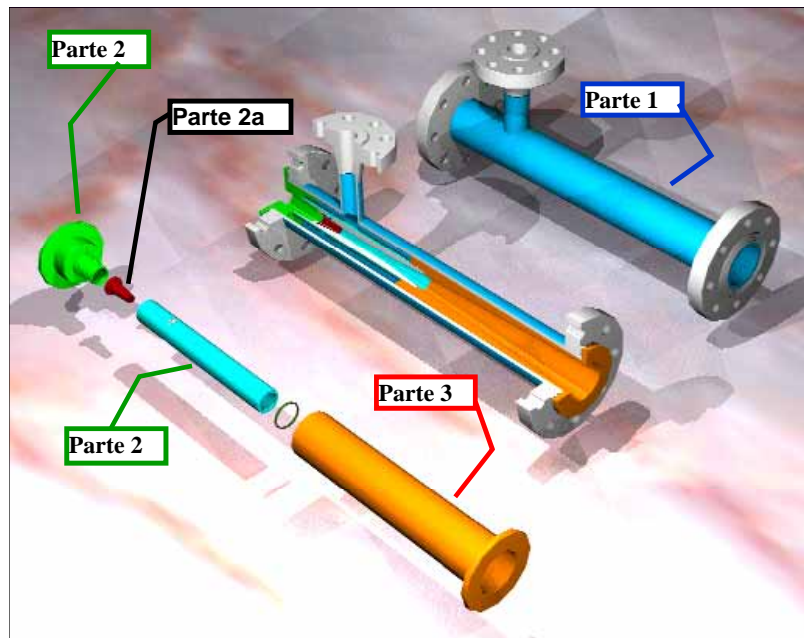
Corte esquemático del Jet de Superficie, despiece
